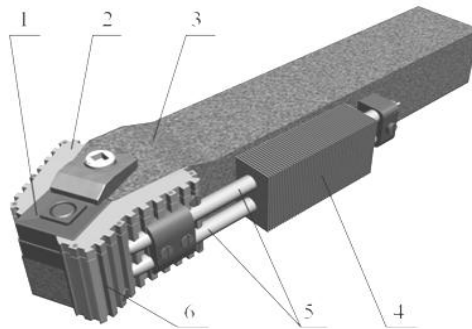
Сборный резец ПТ, оснащенный ТТ
